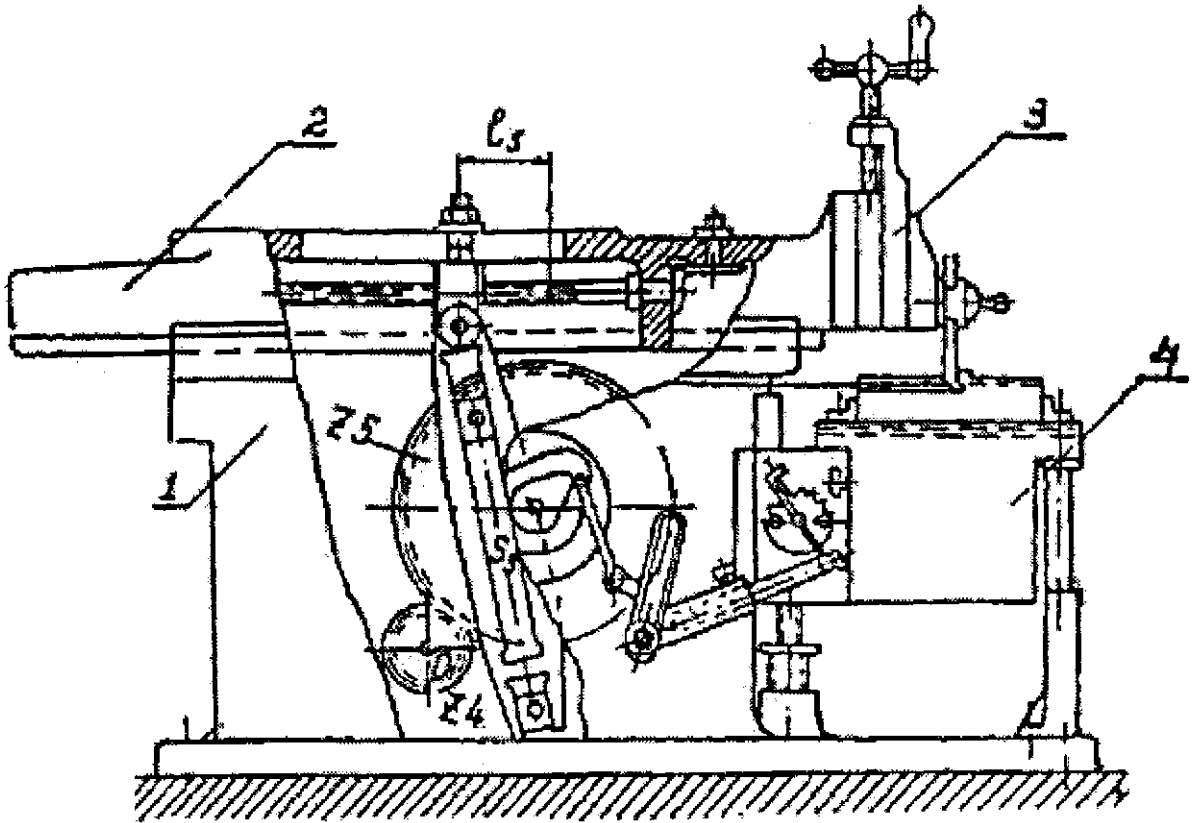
Общий вид поперечно-строгального станка с качающейся кулисой
